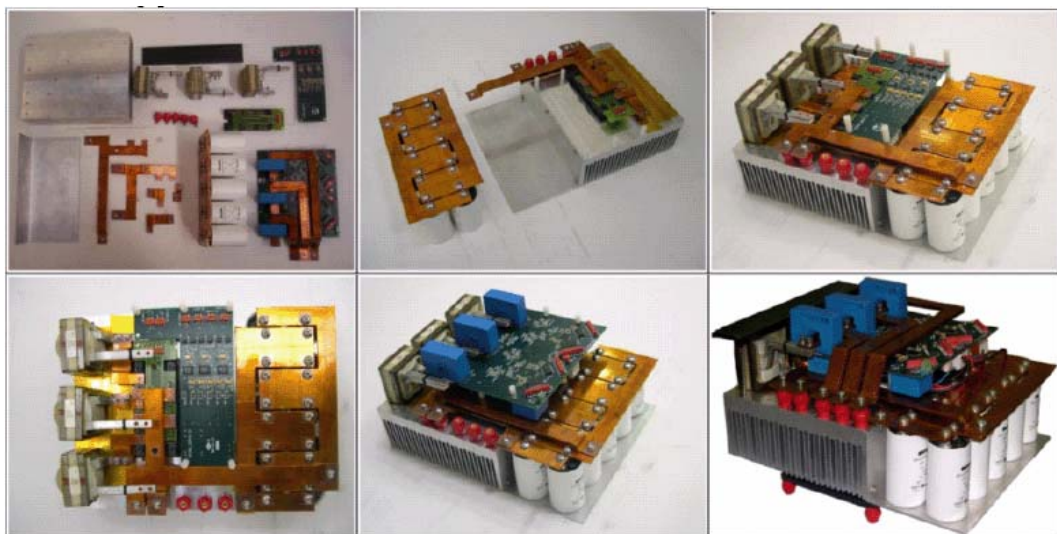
Fasi di assemblaggio di un modulo LV-PEBB
